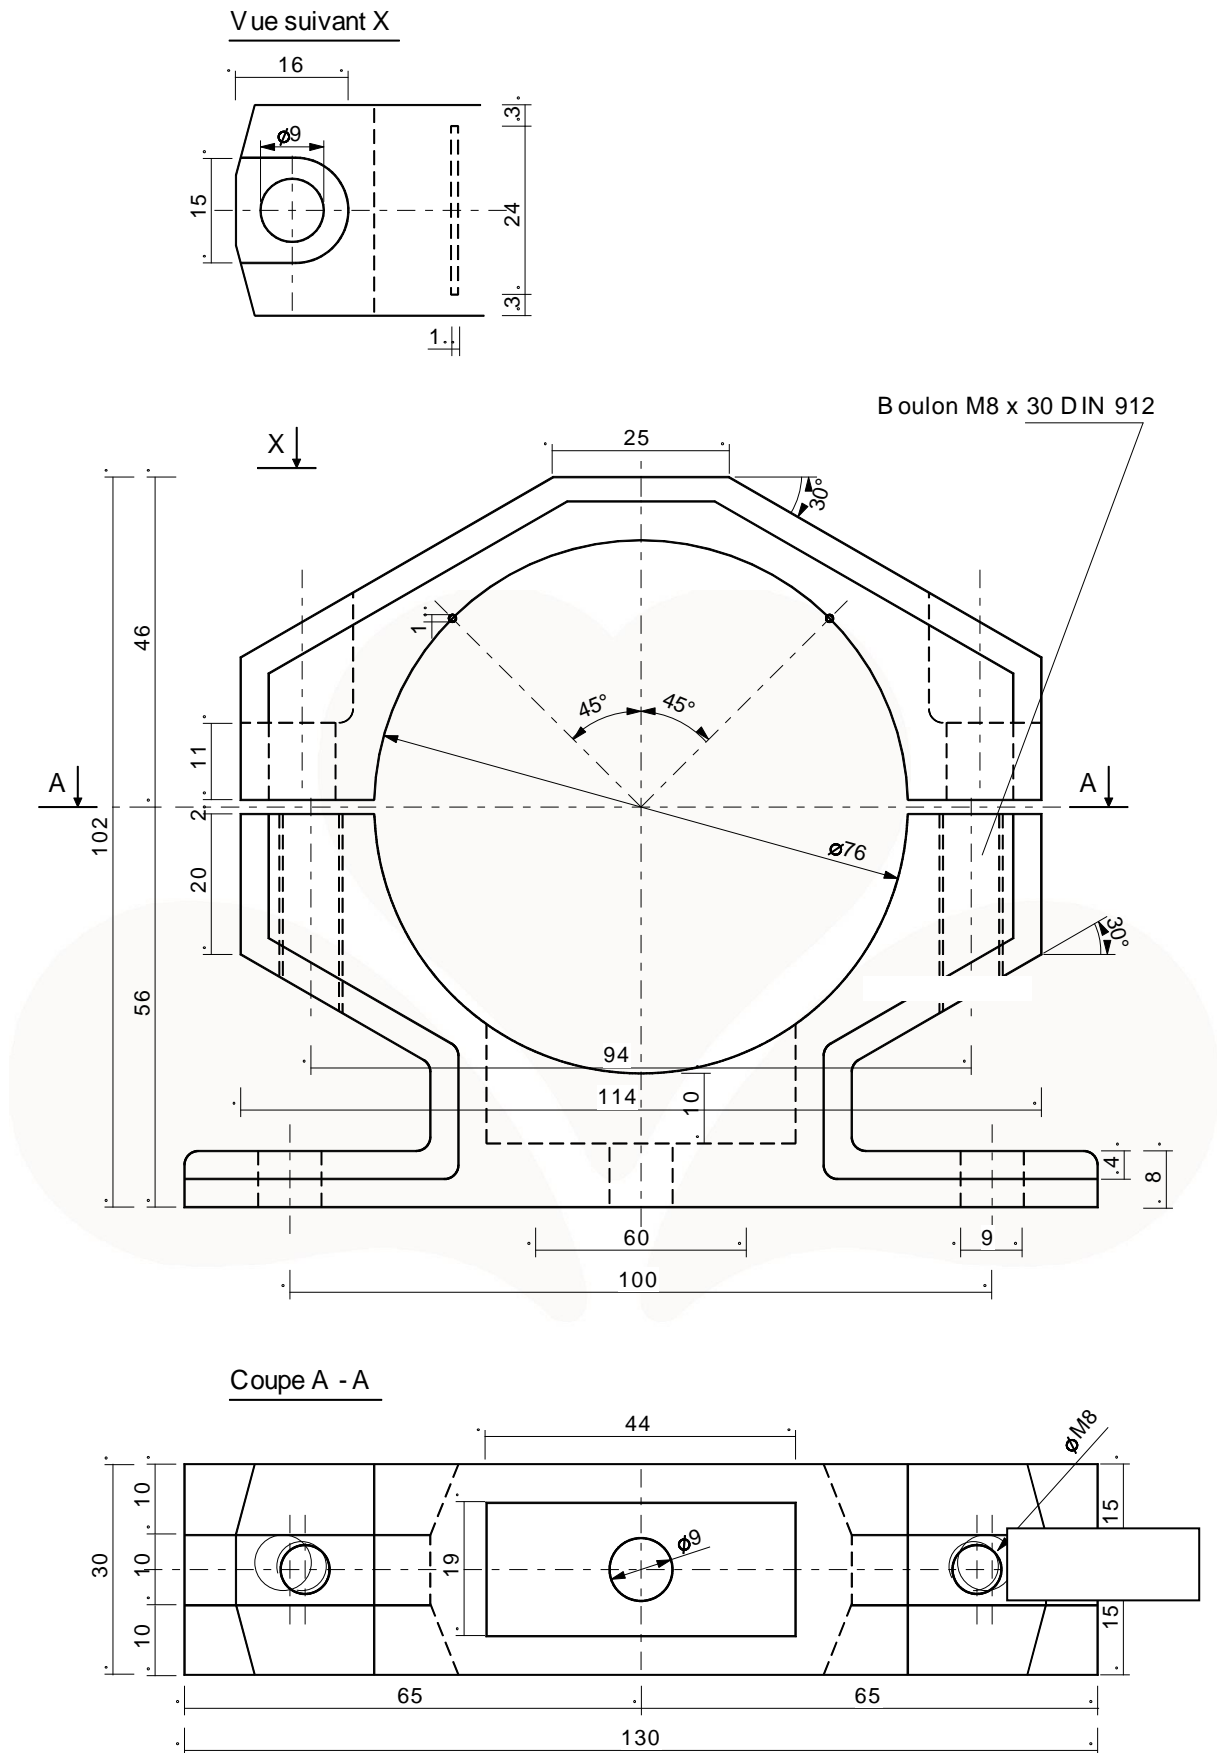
e - Collier pour la fixation d'un panneau au poteau
